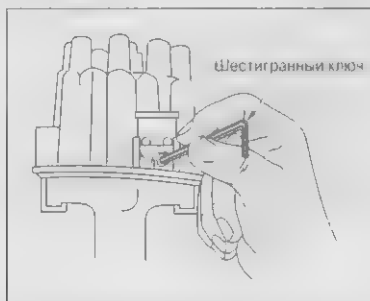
Регулировка контактов прерывателя через регулировочное отверстие
